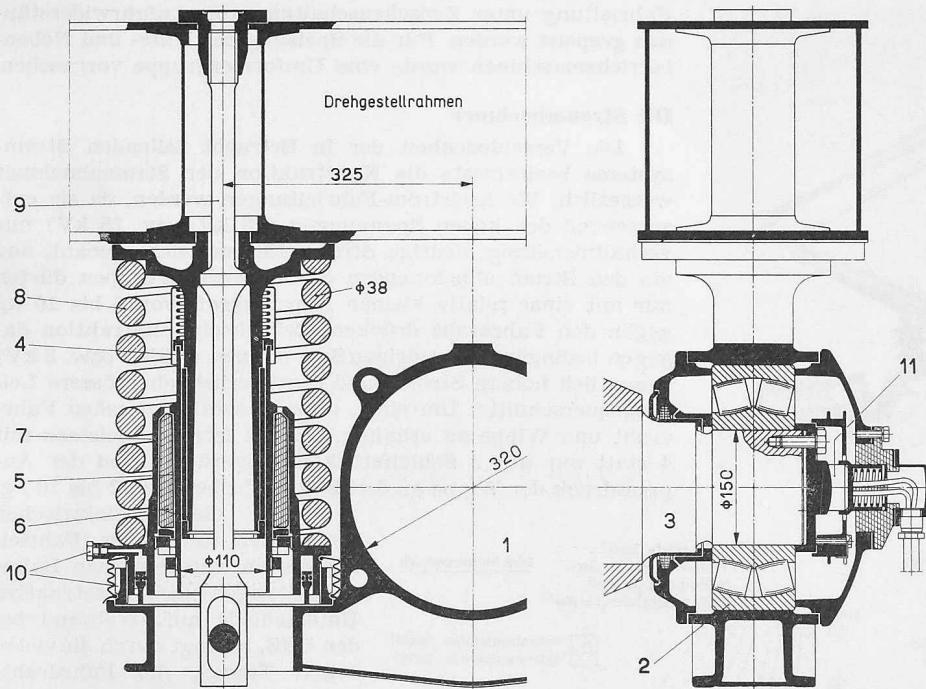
Achslager-Führung und -Federung der Laufachse zum Triebgestell
